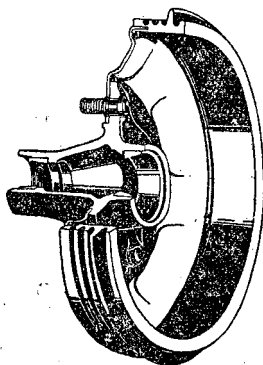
Тормозной барабан и ступица переднего колеса в сборе.
